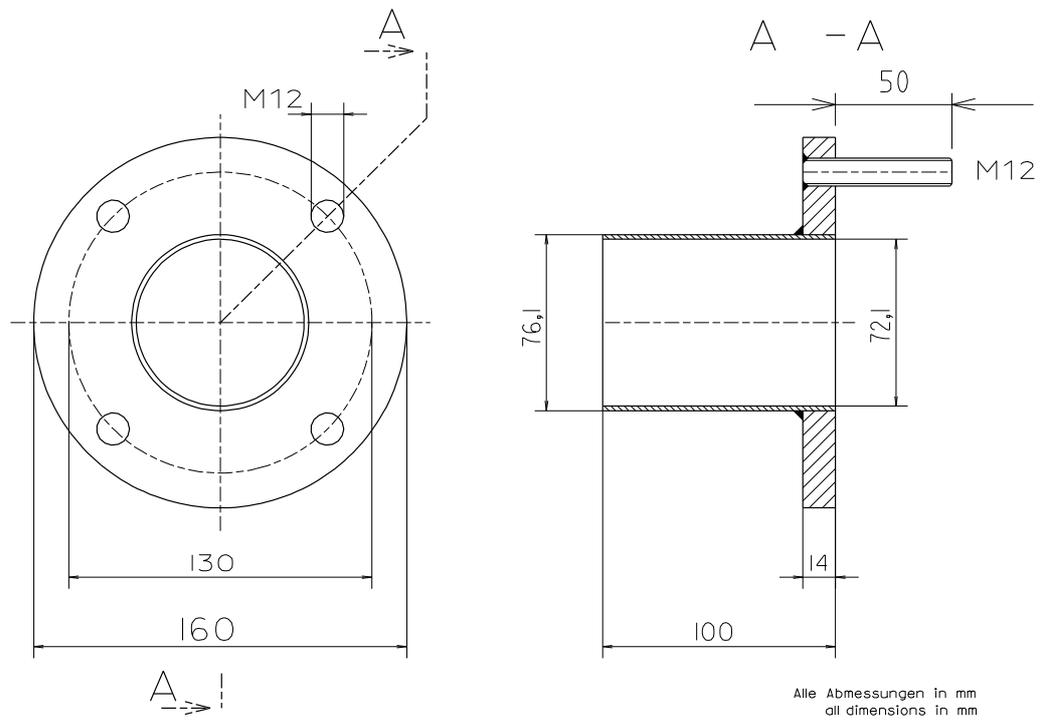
Maßblatt Flansch ADP-1000 passend zu DN 65 PN 6
